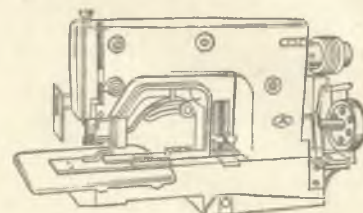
Машина-полуавтомат 220 кл. для изготовления закрепок
